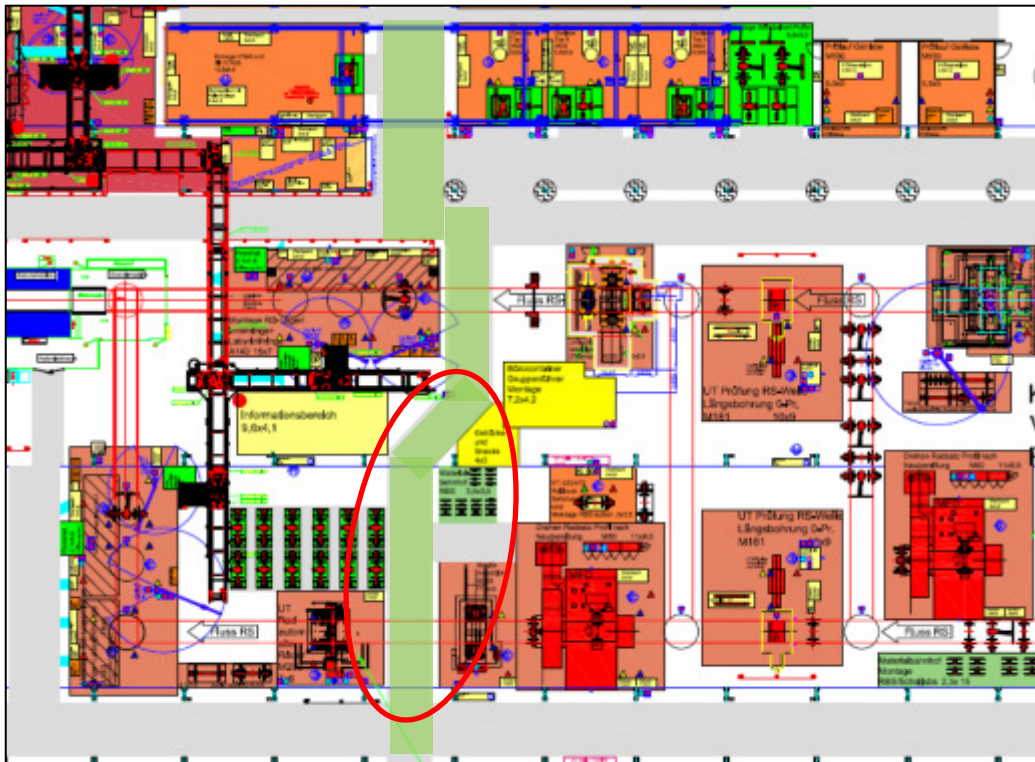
Ausschnitt Maschinenstraße Schiff VII im Bereich des südlichen Gebäudezugang (Mitte)
